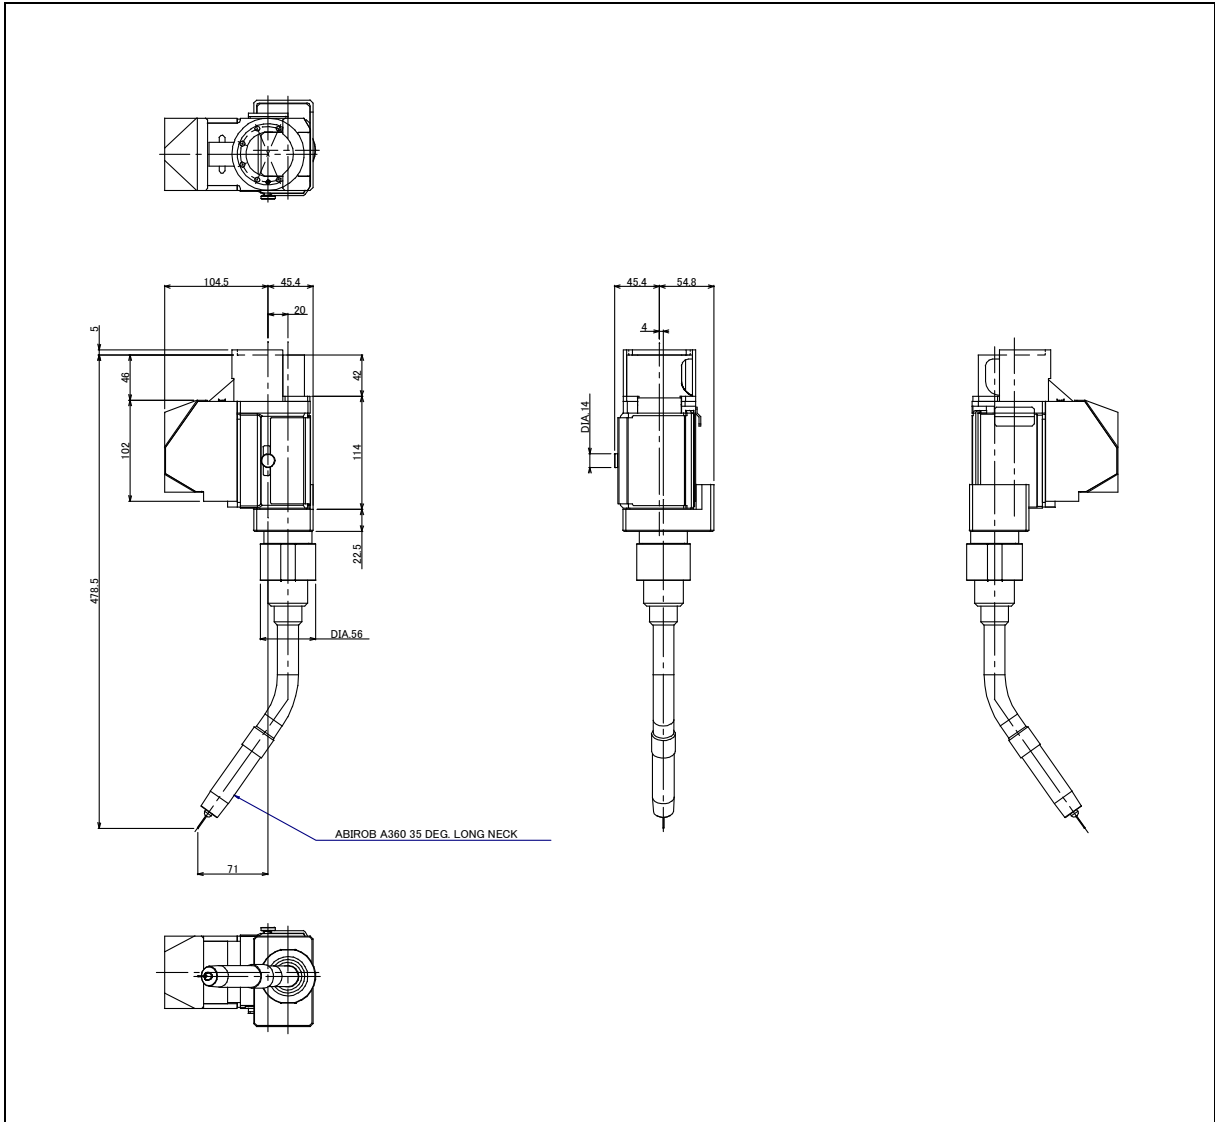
(b) 外形尺寸 (软钢用伺服焊炬)
